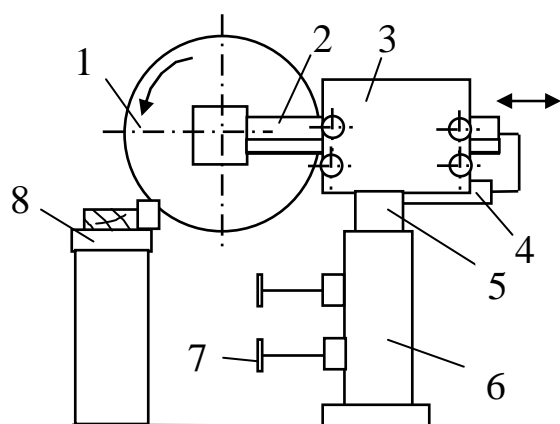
Схема суппортного торцовочного станка ЦПА40
